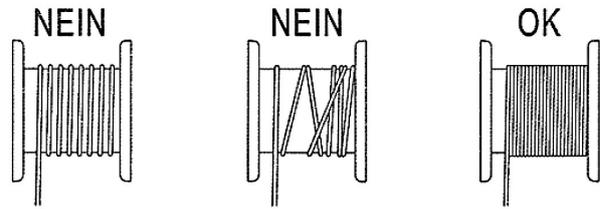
Gleichmäßiges Aufrollen des Kabels beachten
